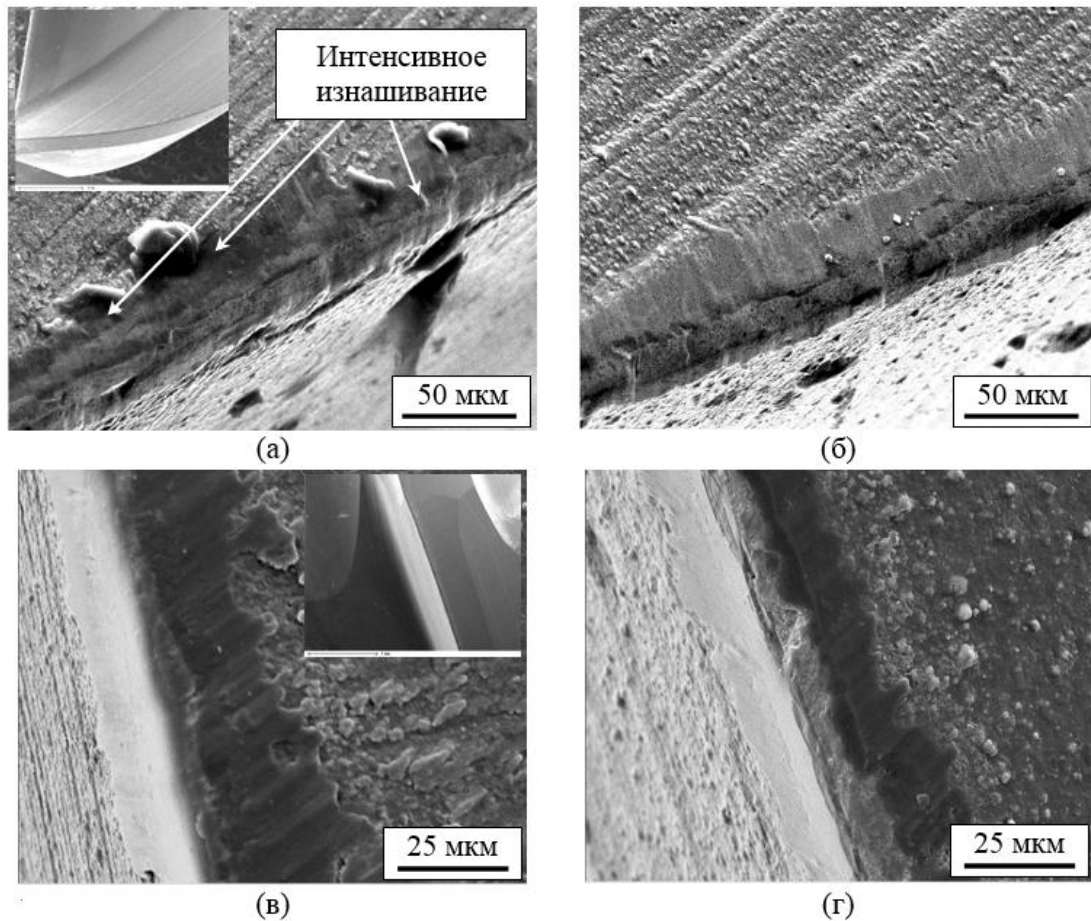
Износ концевой фрезы ТТ8К6 (сталь 40Х; $l = 1\ 050$ м): передняя поверхность фрезы (а, б); задняя поверхность фрезы (в, г); фреза с фаской 50 мкм (а, в); фреза с фаской 150 мкм (б, г)
